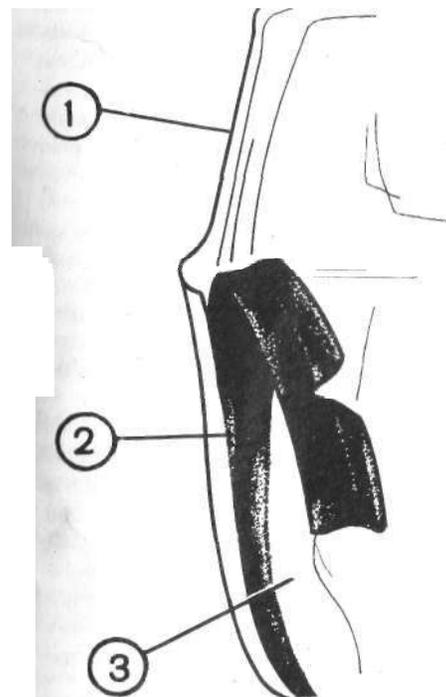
Уплотнитель переднего крыла: 1 — крыло; 2 — уплотнитель; 3 — щиток
